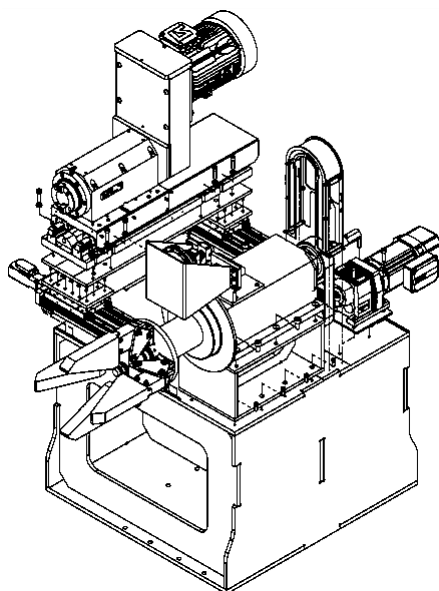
Perspetiva isométrica explodia do desenho de conjunto “Assembly final CF”.
